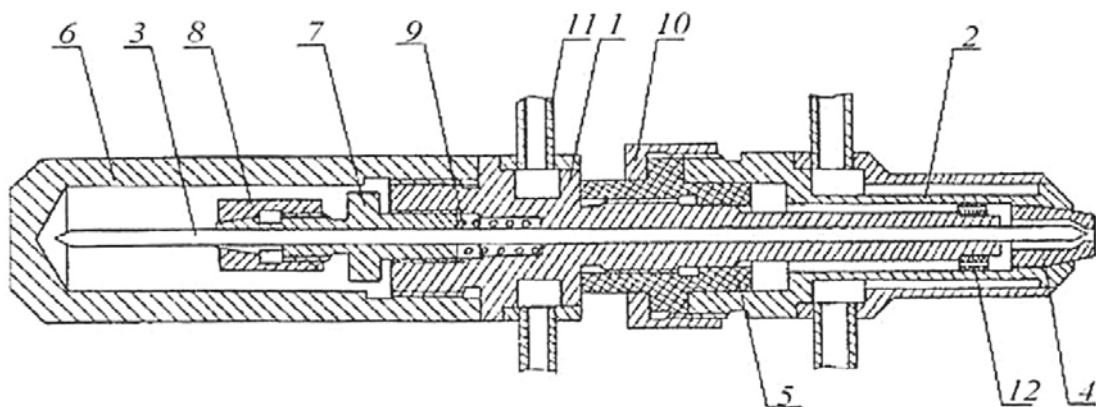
Общий вид плазматрона для сварки тонкостенных труб:
